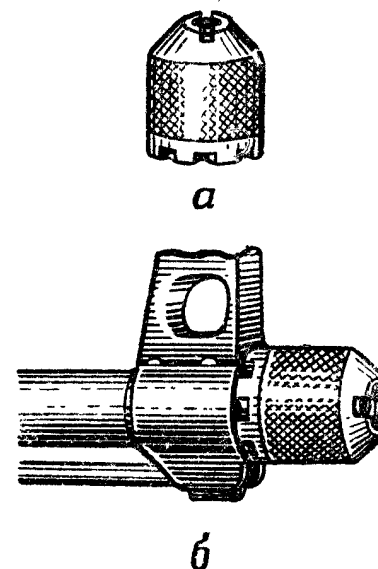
Втулка для стрельбы холостыми патронами из автомата и ручного пулемета Калашникова:
